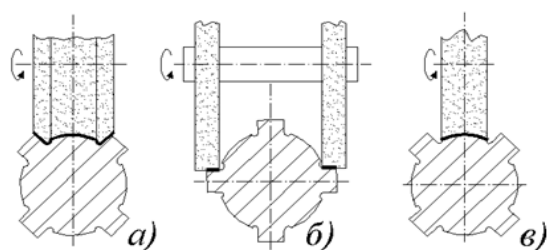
Схемы шлифования шлицев: всего профиля фасонным кругом (а); боковых поверхностей (б); внутренней поверхности (в)
